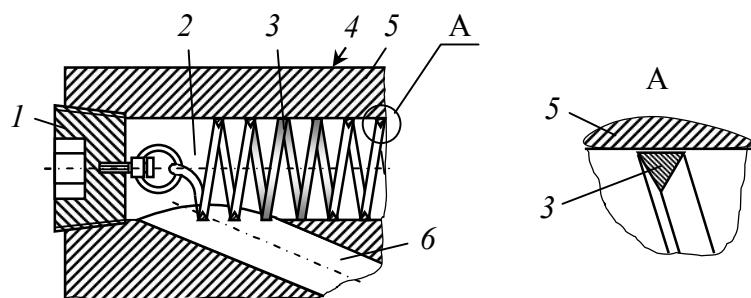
Конструкція турбулізатора периферійного каналу згідно з пат. України № 78653 U [105]: 1 – торцева нарізна пробка; 2 – периферійний канал; 3 – пружина – турбулізатор; 4 – робоча поверхня валка; 5 – бочка; 6 – похилий канал
